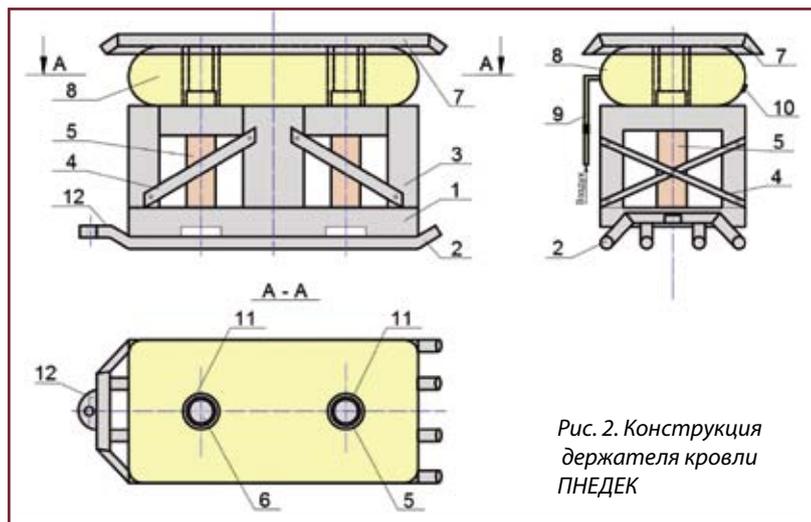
Конструкция держателя кровли ПНЕДЕК
